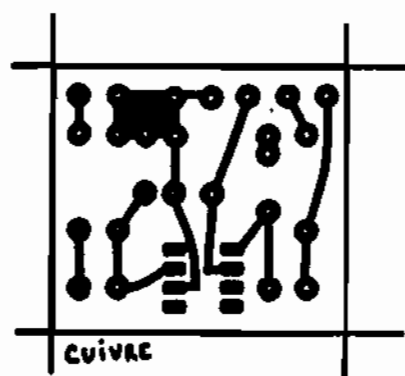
Circuit imprimé, côté soudure.
